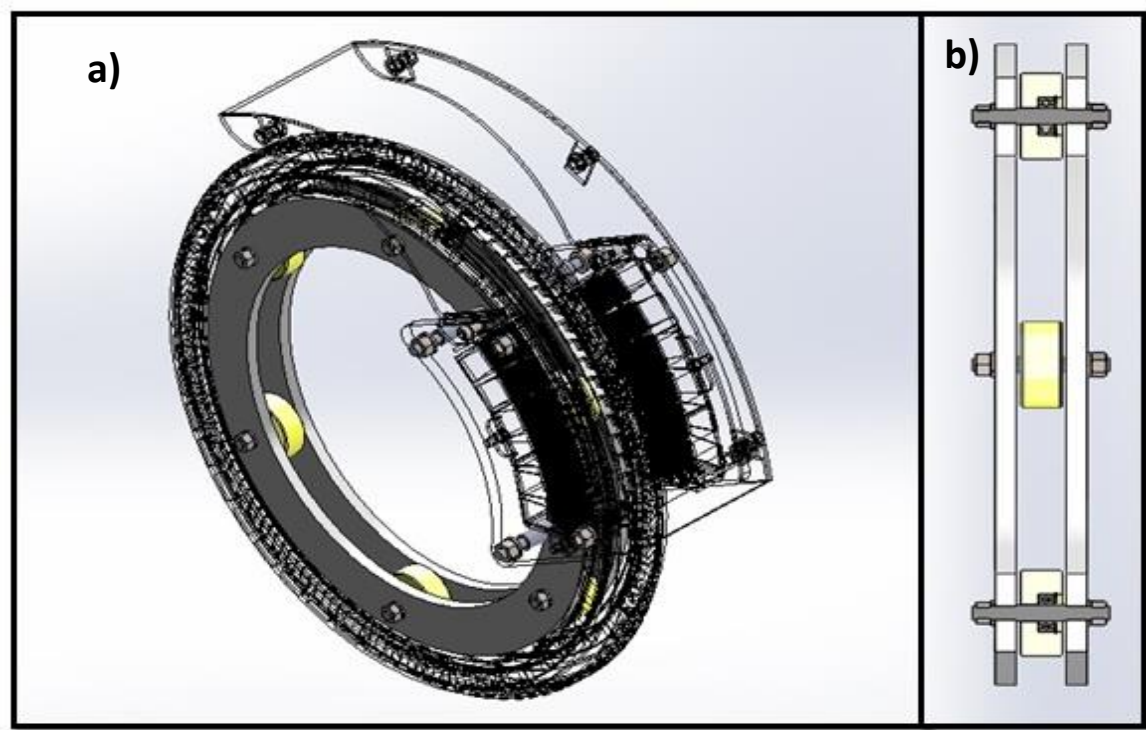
Vistas del Subensamble del Rodamiento. a) vista isométrica y b) vista frontal.
